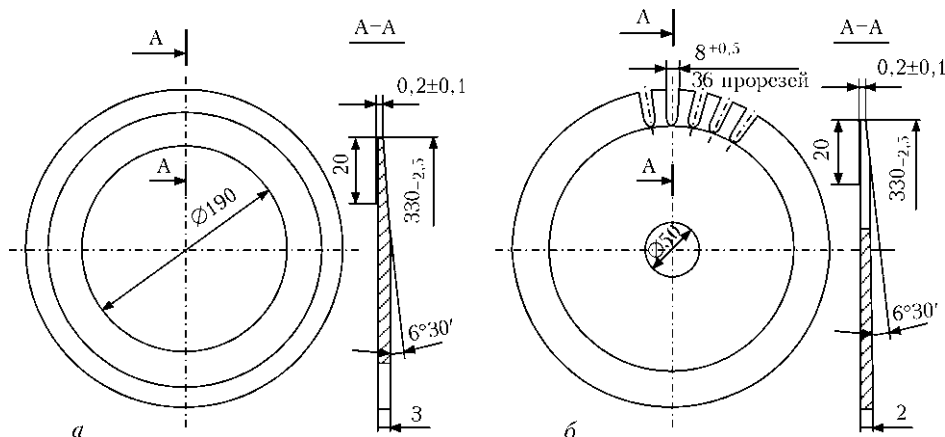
Схема конструкции дисковых ножей [12]: а — неприводной; б — приводной
